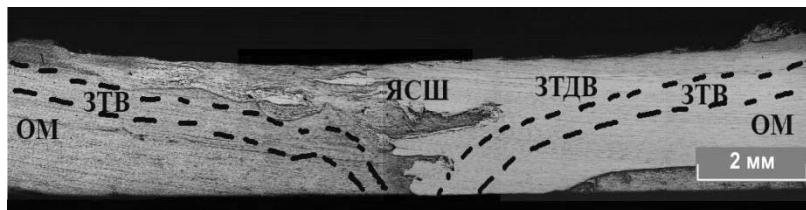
Макрошлиф сварного шва алюминия и меди (режим 4)
